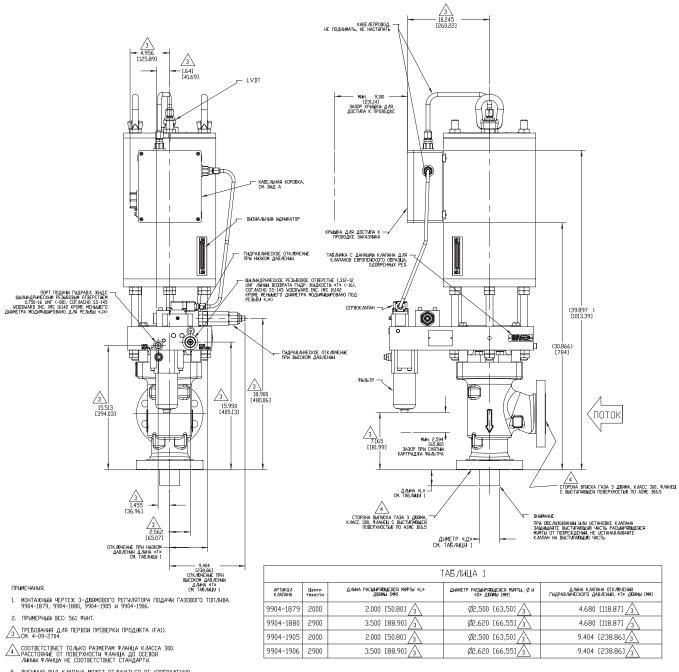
а. Габаритный чертеж регулятора SonicFlo (3 дюйма, класс 300)
